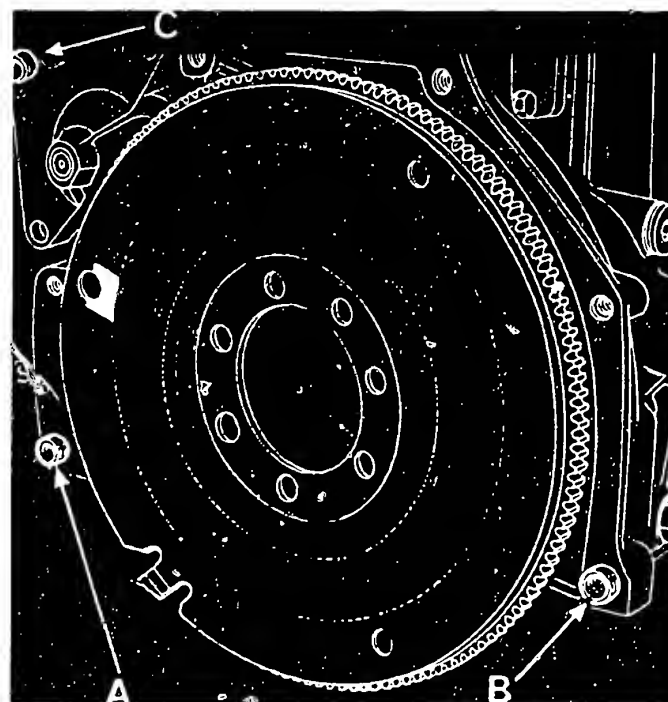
Vor dem Einbau des Getriebes ist zu prüfen, ob die Hülse A, B und C eingebaut sind.
